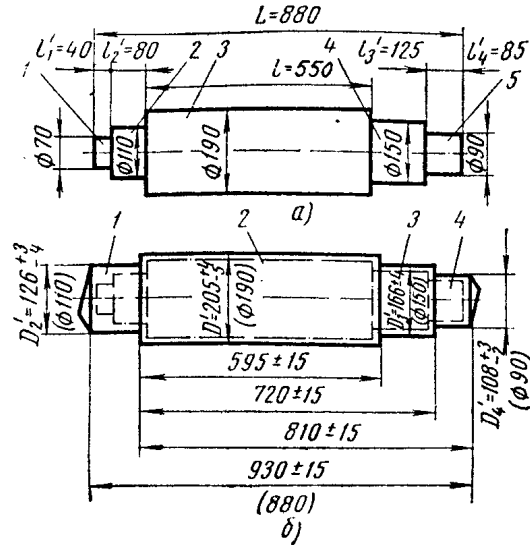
Чертежи сплошного вала с уступами (а) и поковки этого вала (б)
